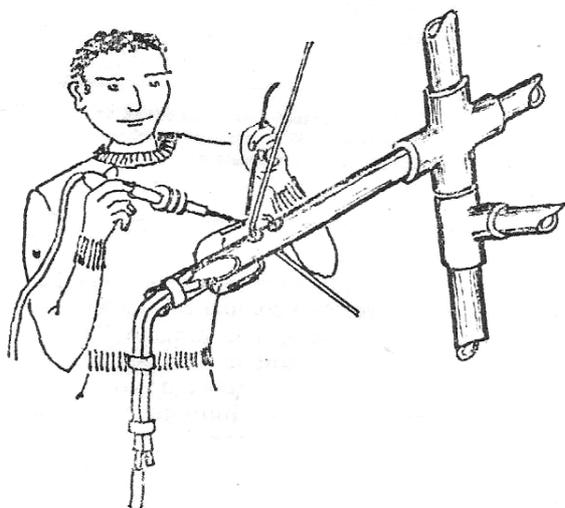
Soldando o balun e o cabo coaxial ao elemento irradiante (é preciso soldar por causa da chuva!).
